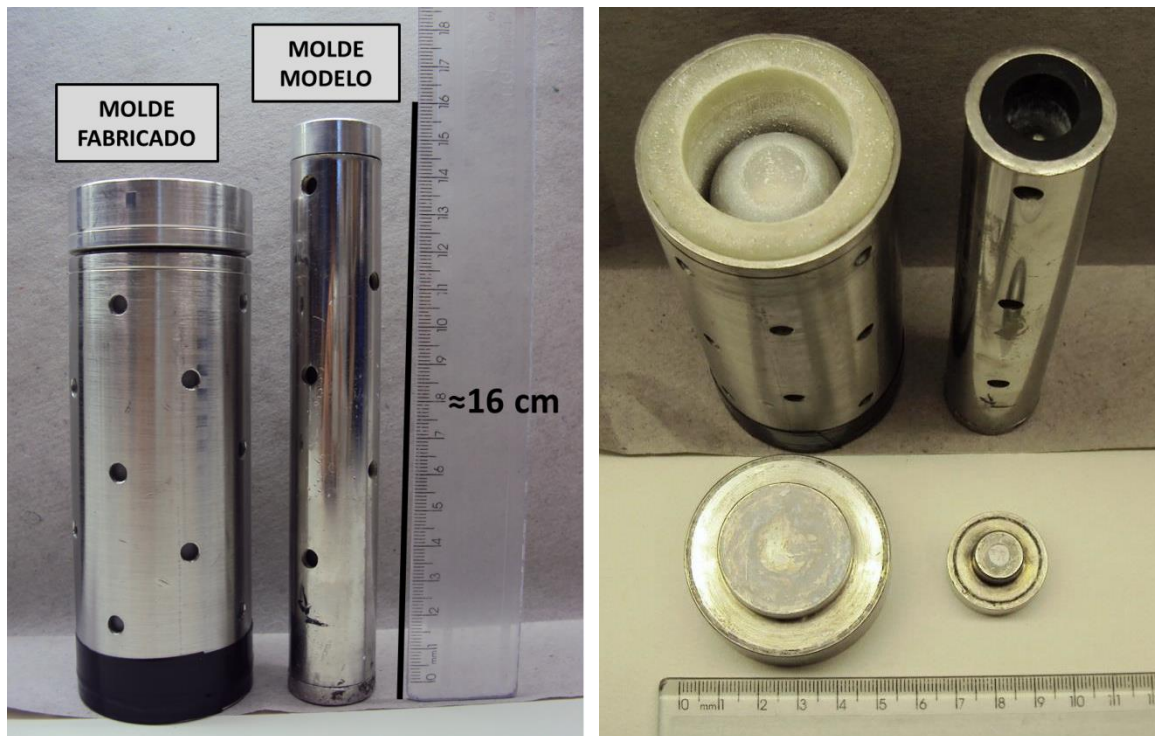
Imagem do molde fabricado e do molde modelo.
